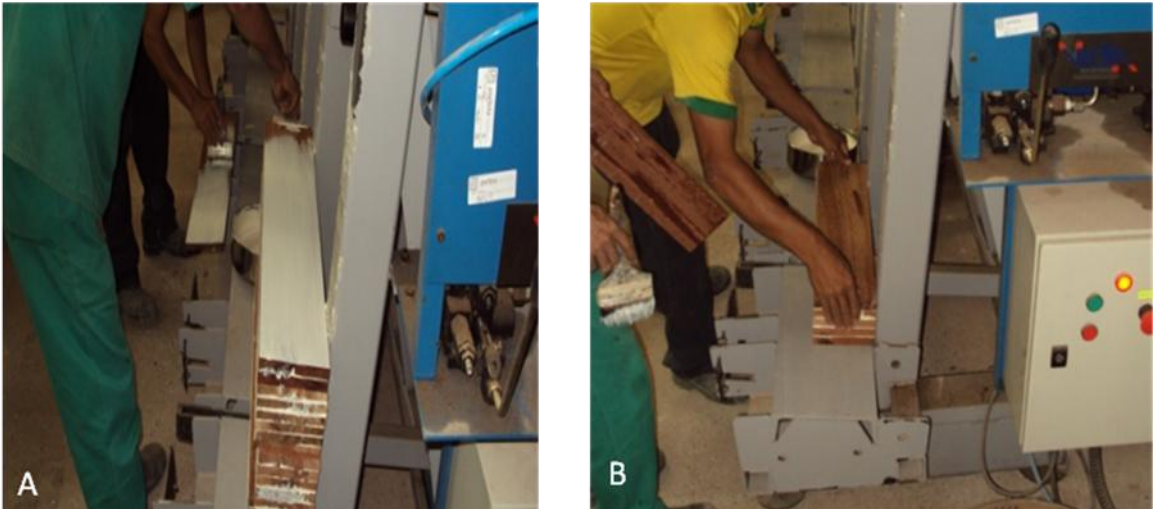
A - Aplicação da cola, B - Montagem da viga
